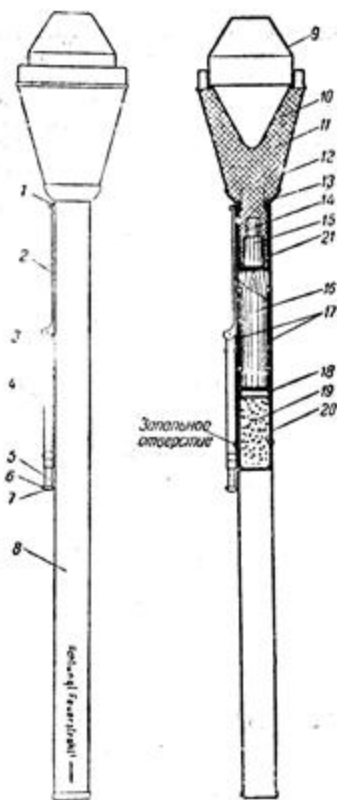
Реактивное противотанковое приспособление большого образца — „Фаустпатрон-2“:
